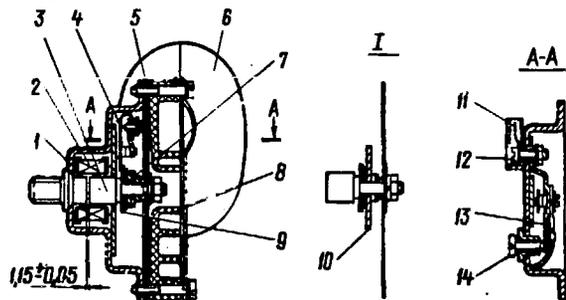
Звуковой сигнал: 1 - корпус; 2 - обмотка сердечника; 3 - якорь; 4 - упругая пластина; 5 - мембрана; 6 - крышка диффузора; 7 - груз; 8 - корпус диффузора; 9 - шайба; 10 - груз; 11 - штекер; 12 - винт; 13 - держатель; 14 - регулировочный винт; I - якорь с мембраной сигнала высокого тона
